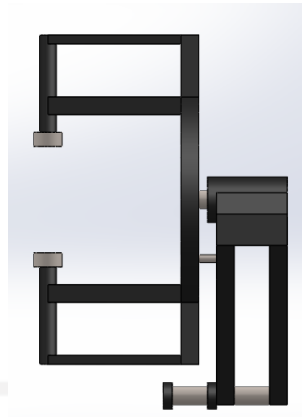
21 Tampak Isometris (Dudukan Konveyor Posisi Terbuka Pada Alat)
